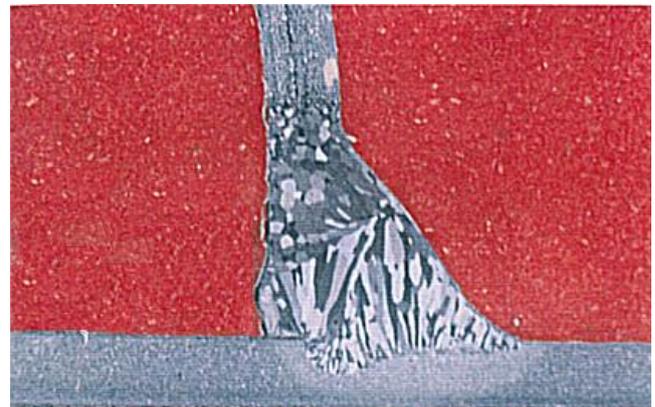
T字すみ肉溶接部のマクロ組織
